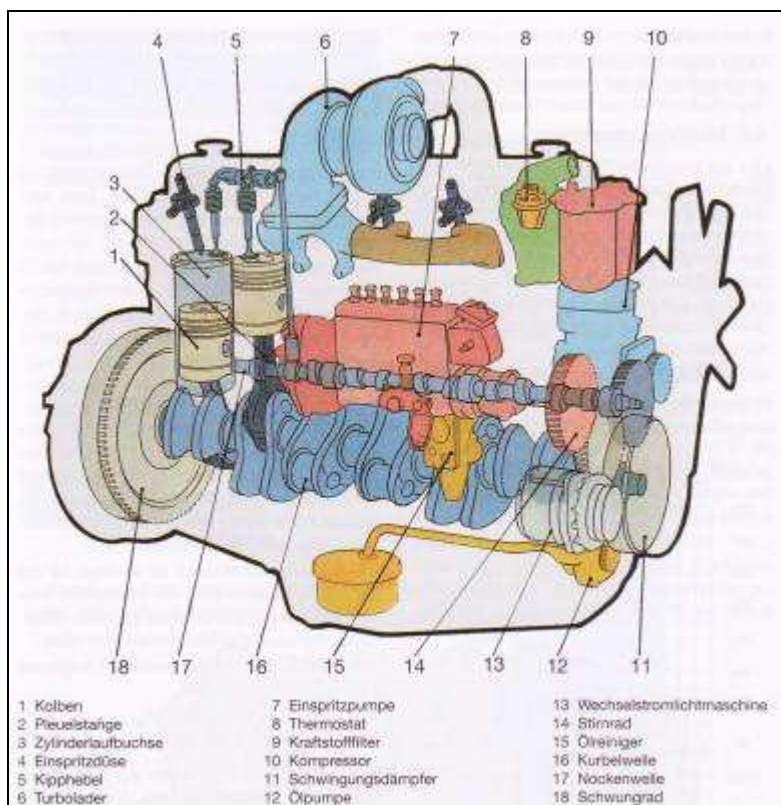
Komponenten eines Dieselmotors; Quelle: [Q 41]
